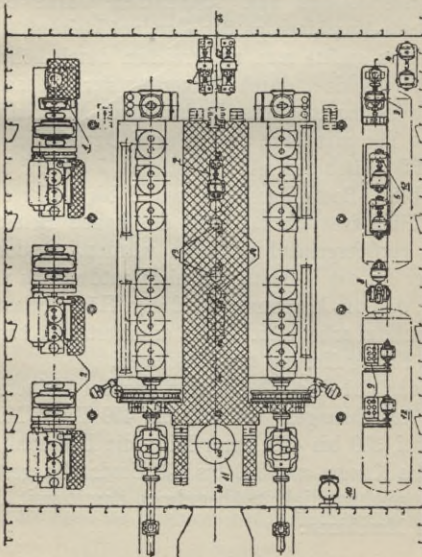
Maschinenanlage der Doppelschraubenmotorschiffe „Isis“ und „Osiris“. Schiffe gebaut von der Deutschen Werft, Hamburg; Antriebsmaschinen: je zwei Burmeister & Wain-Viertaktschiffsdieselmotoren (Ausführung A. F. G.).
